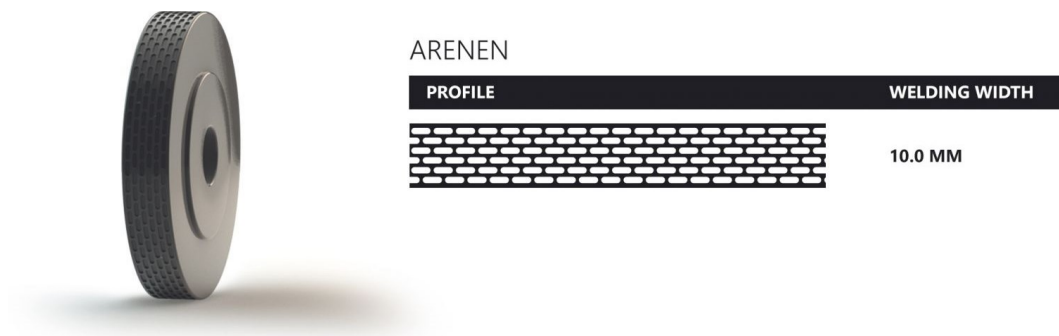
Laufrad-Aufsatz für durchgängige 10 mm Schweißnaht; Quelle: jentschmann.ch
